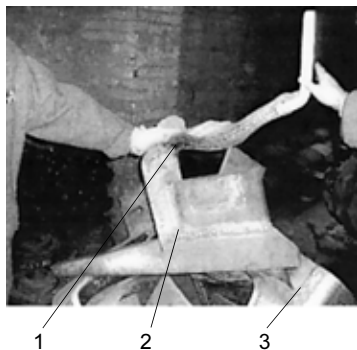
Конструкция узла шинопровода, сваренная полуавтоматом ПШ 107 ВА с импульсной подачей: 1 — сварка гибкой связи; 2 — угловые швы; 3 — стыковой шов
